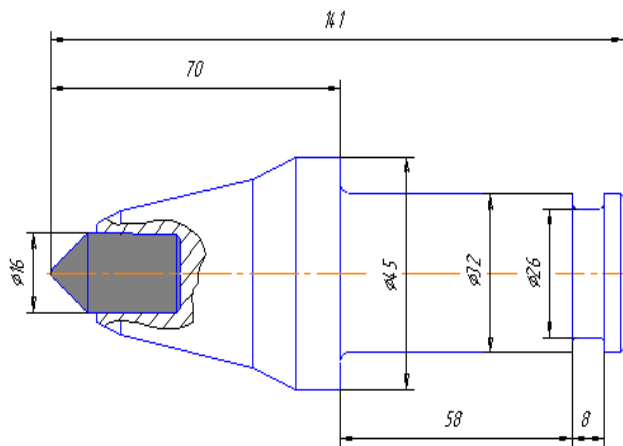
Тангенциальный поворотный резец РШ 32-70/16Х со вставкой из износостойкой стали
